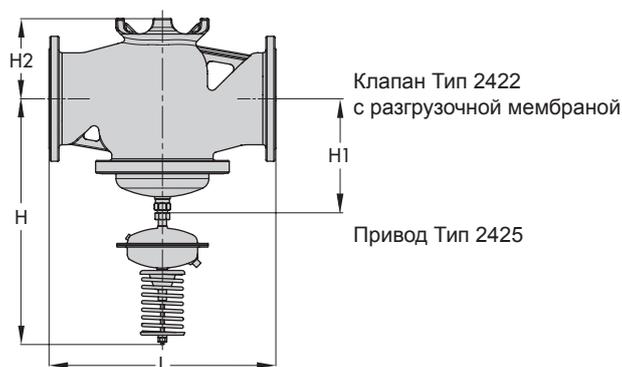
Габаритный чертёж, клапан Тип 2422 с разгрузочным сифоном с приводом Тип 2425
